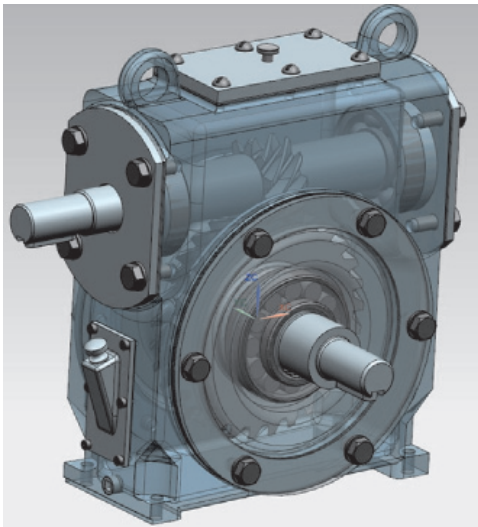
Модель редуктора с гиперболическими зубчатыми колесами
